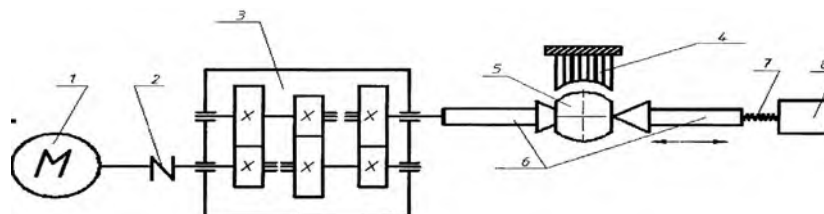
Кинематическая схема автомата для контроля дефектов: 1 - электродвигатель; 2 - муфта; 3 - редуктор; 4 - фотоэлектрический датчик; 5 - деталь; 6 - вращающиеся центра; 7 - пружина; 8 - электромагнит
